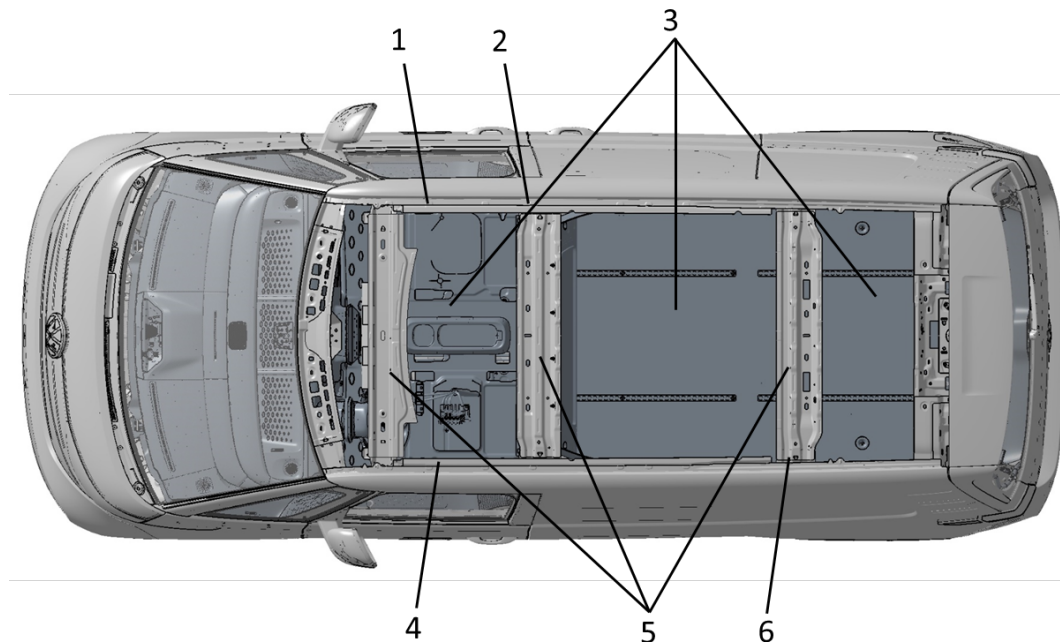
Nachträgliche Dachausschnitte (Prinzipdarstellung)
